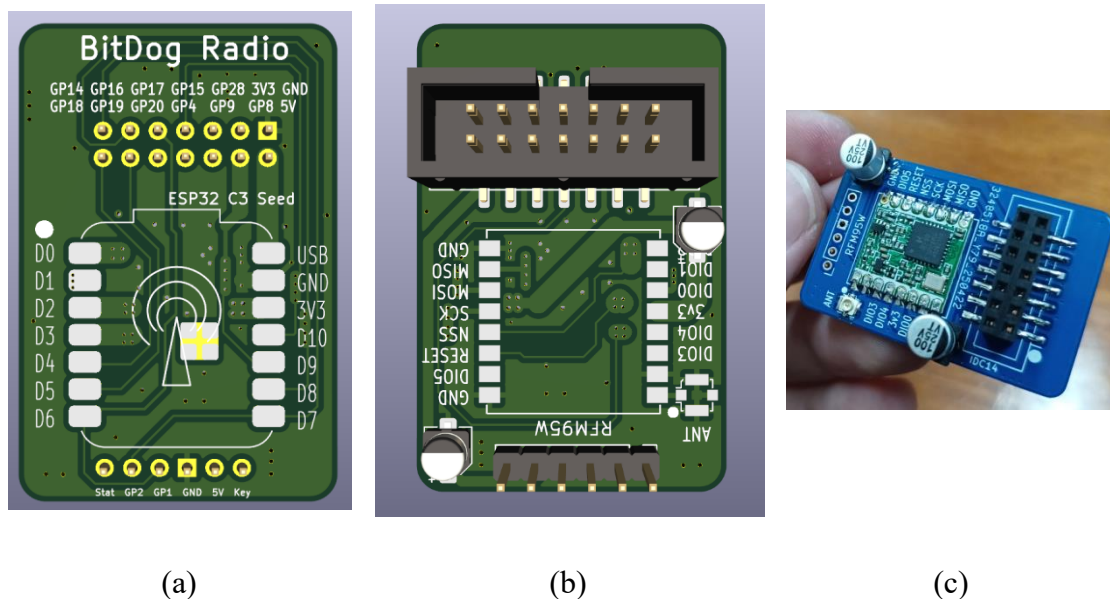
Layout do módulo Wireless (a) Backside (b) Frontside (c) Módulo montado
